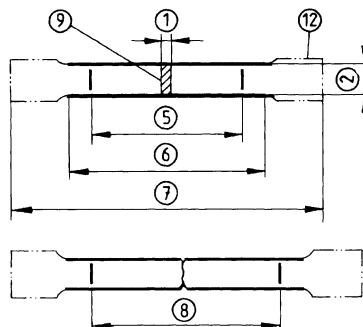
Bearbeitete Proben mit rechteckigem Querschnitt (Anhang B der Norm)
